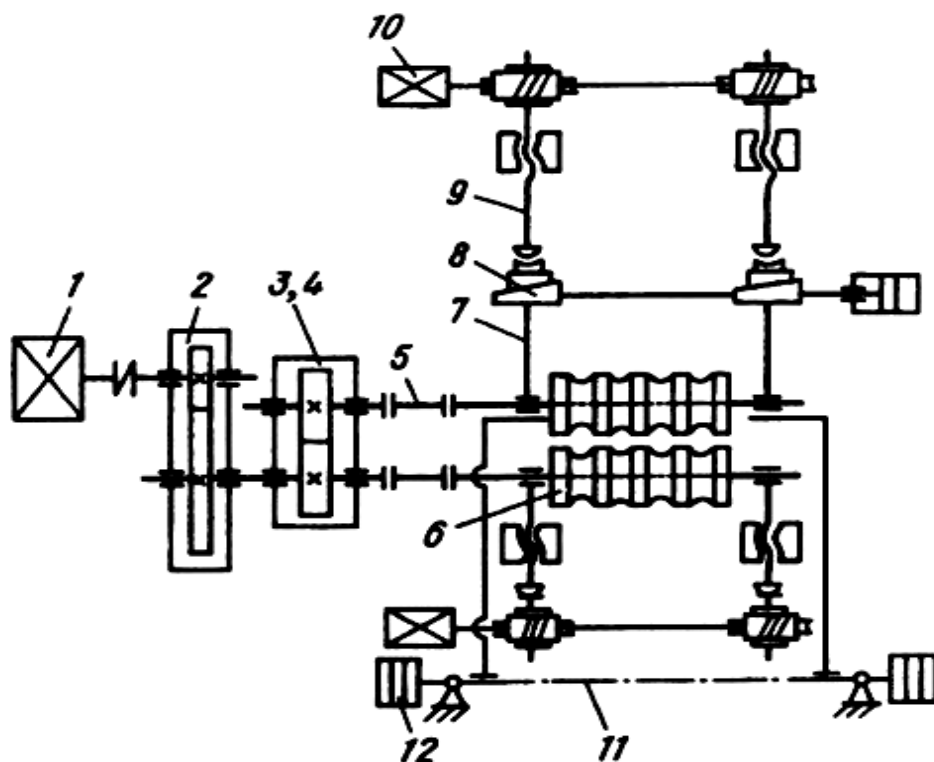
Схема головної лінії автомат-стану і механізмів кліті: 1 - електродвигун приводу валків 2 циліндричний редуктор; 3 - маховик (може бути відсутнім); 4 - шестеренна кліть; 5 шпиндель; 6 робочі валки; 7- натискний пристрій; 8 - клиновий механізм; 9 - натискний гвинт; 10 привід переміщення верхнього валка; 11 - урівноваження верхнього валка 12 - гідроциліндр врівноваження.
